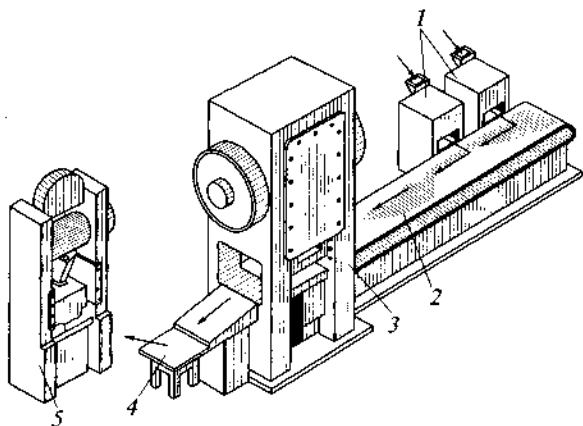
Схема расположения оборудования в поточной линии для штамповки поковок:
